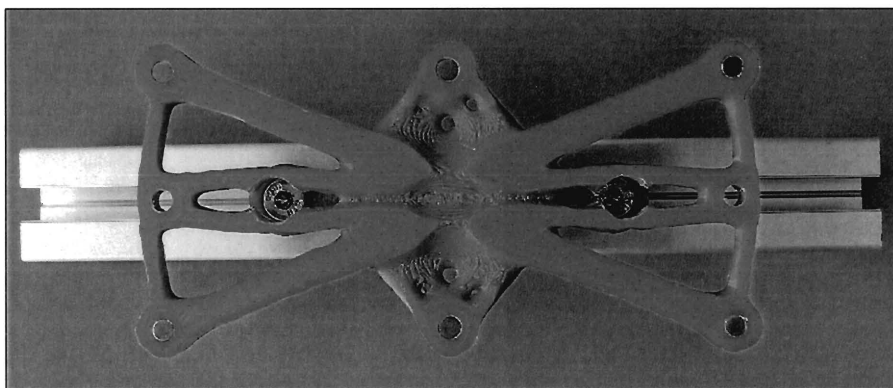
Element de prindere montat pe profil de aluminiu – TIP 1
